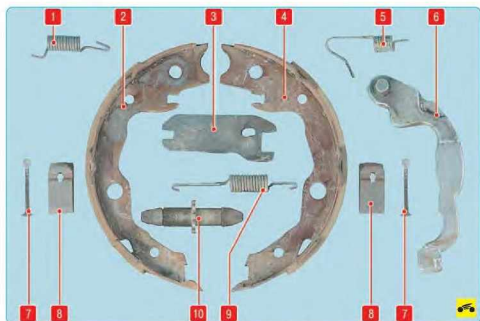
Детали тормозного механизма стояночного тормоза (на фото показаны детали тормозного механизма левой стороны): 1 – верхняя стяжная пружина передней колодки; 2 – передняя колодка стояночного тормоза; 3 – разжимная планка; 4 – задняя колодка стояночного тормоза; 5 – верхняя стяжная пружина задней колодки; 6 – разжимной рычаг; 7 – опорная стойка; 8 – пружинный фиксатор опорной стойки; 9 – нижняя стяжная пружина колодок; 10 – регулировочное устройство тормозных колодок стояночного тормоза
